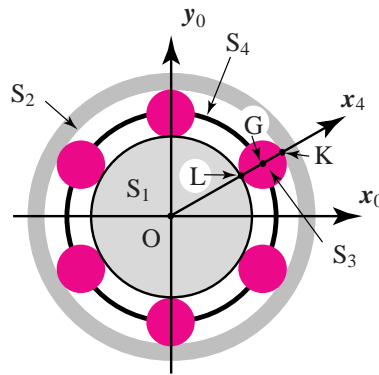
Roulement à aiguilles. Vue en coupe avec les chemins de roulement interne et externe, les rouleaux et la cage.
